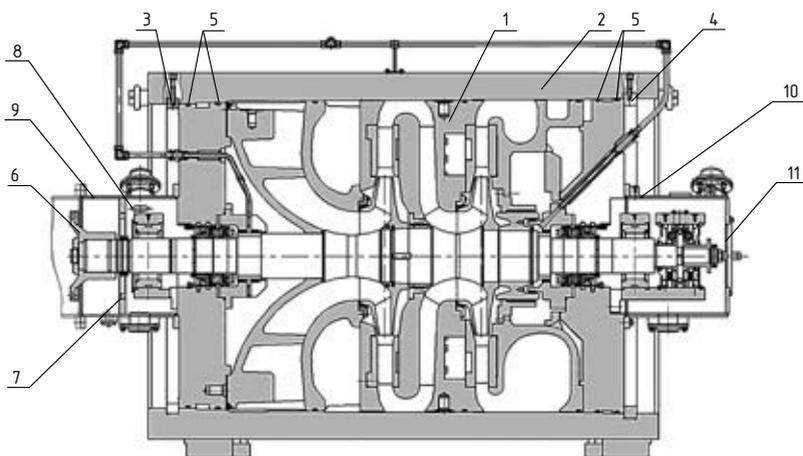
Продольный разрез компрессора: 1 – пакет; 2 – цилиндр; 3 – кольцо из 8 частей; 4 – кольцо из девяти частей; 5 – уплотнительные кольца; 6 – втулка фланцевая; 7 – обойма уплотнения; 8 – верхняя половина блока опорного вкладыша; 9 – верхняя половина кожуха опорного подшипника; 10 – верхняя половина кожуха опорно-упорного подшипника; 11 – крышка
